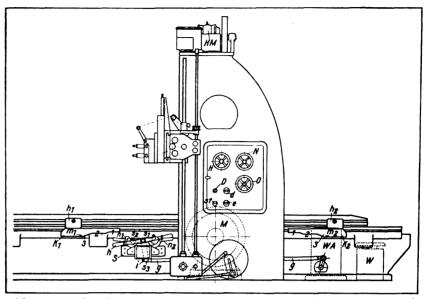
Umrißzeichnung einer Hobelmaschine mit elektrischem Antrieb durch Gleichstromwendemotor.
